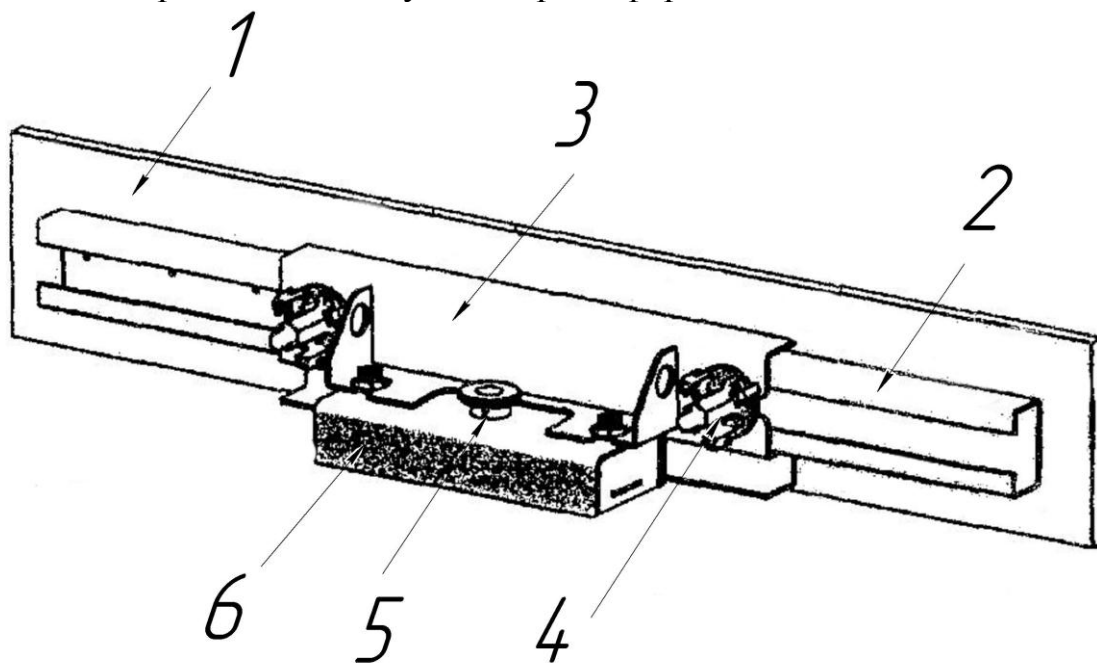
Магнитный фиксатор для крепления борта к поддону:
